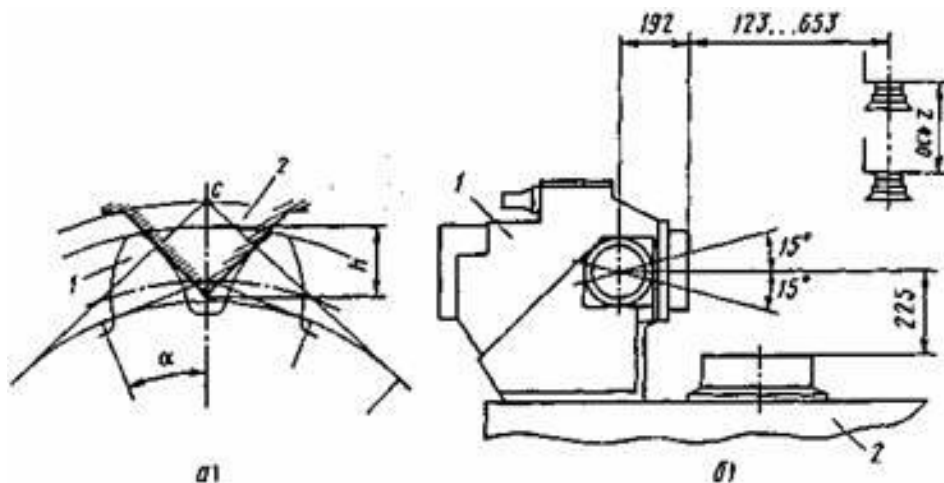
Зацепление зубьев цилиндрических передач (а) и приспособление для обработки колес (б)
